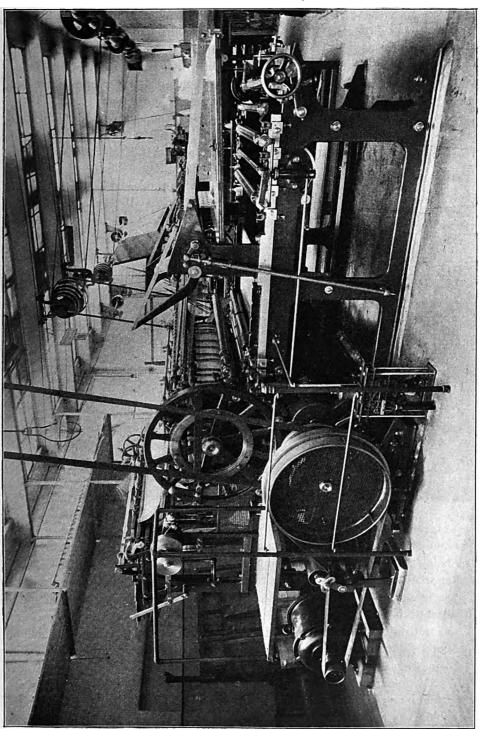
Elektrisch und mechanisch gesteuerte Zweitourenmaschine
